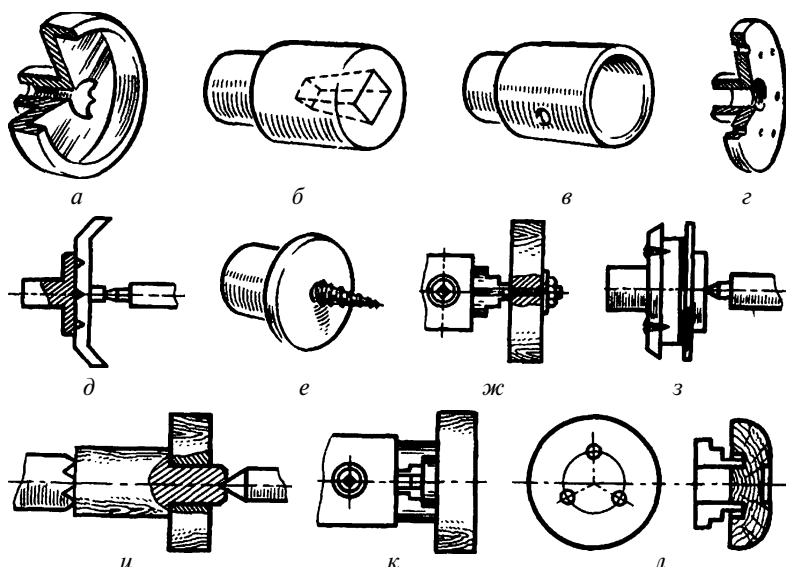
Приспособления и способы крепления заготовок на токарном станке:
